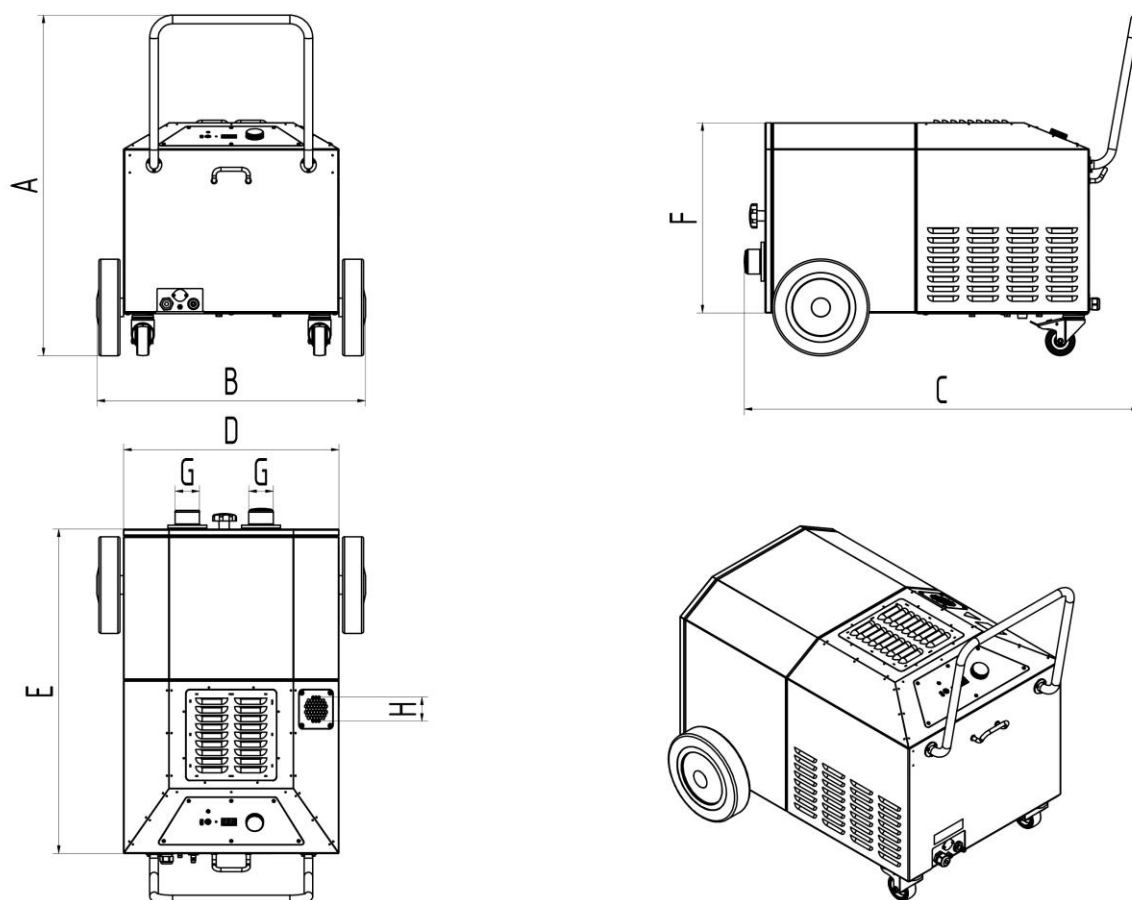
Hoja de dimensiones – Producto sin accesorios
